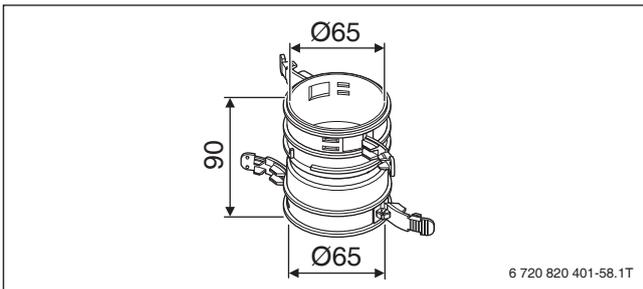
Verbindungsstück Flex Ø 60 mm (Maße in mm)
